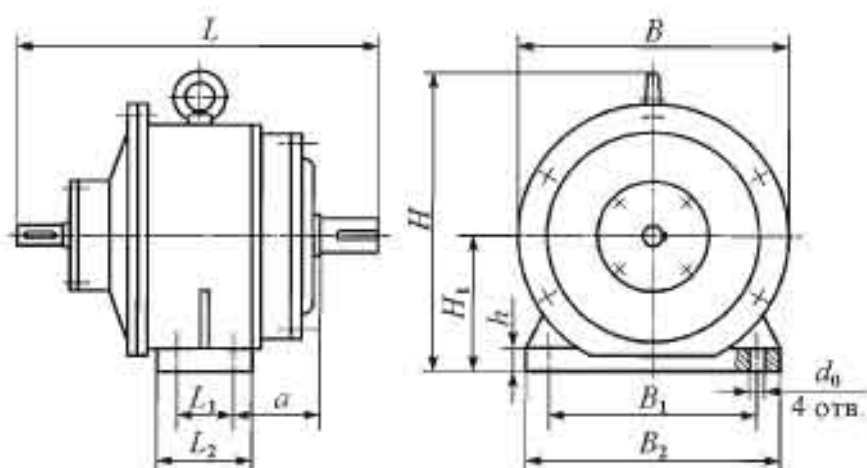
Габаритные, установочные и присоединительные размеры планетарного редуктора
